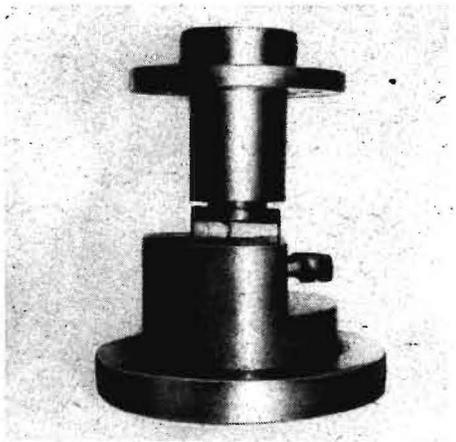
Umformwerkzeug zur Aufarbeitung von Schlepphebeln
